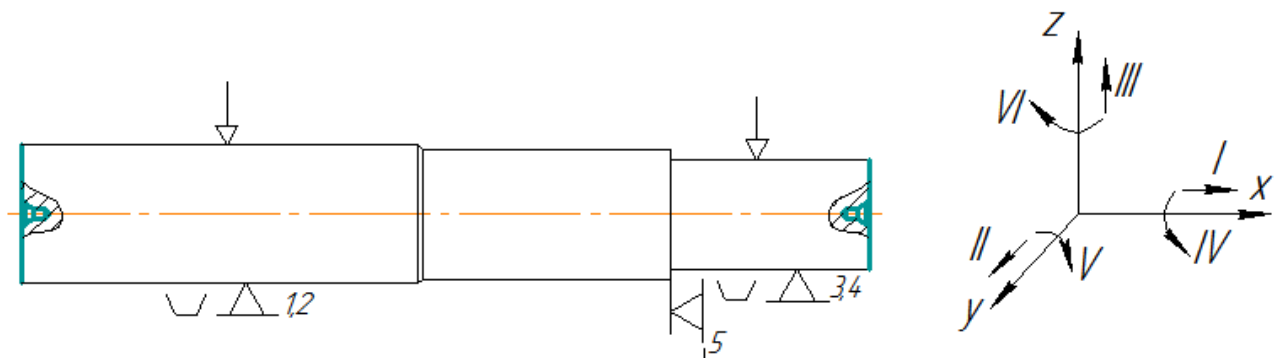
Другий спосіб базування та закріплення заготовки
